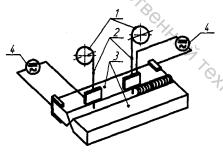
Двухдуговая сварка под флюсом: 1 – намоточные барабаны; 2 – злектроды; 3 – пластины: 4 – источники тока
